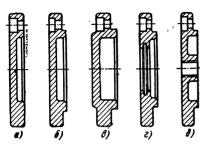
Крышки прижимные для подшипниковых корпусов: а— низкая; б— нормальная; е— высокая; е— с канавкой под уплотнительное кольцо; д— упорная
